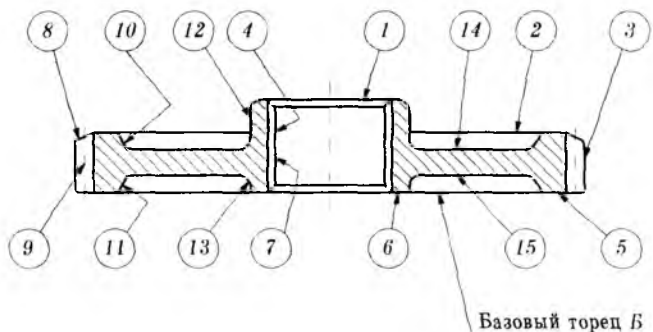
Эскиз зубчатого колеса с нумерацией обрабатываемых поверхностей
